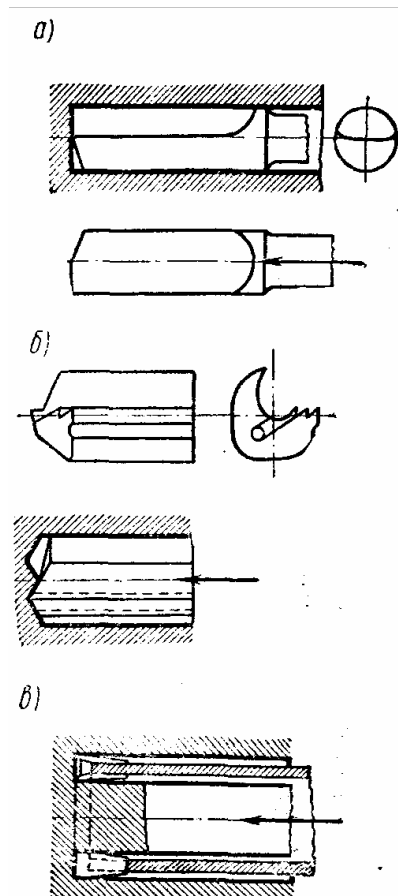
Схемы обработки и виды сверл для глубокого сверления
